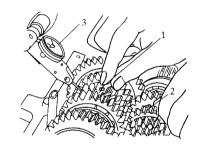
齿轮啮合间隙的检查 1. 齿轮 2. 齿轮 3. 百分表
